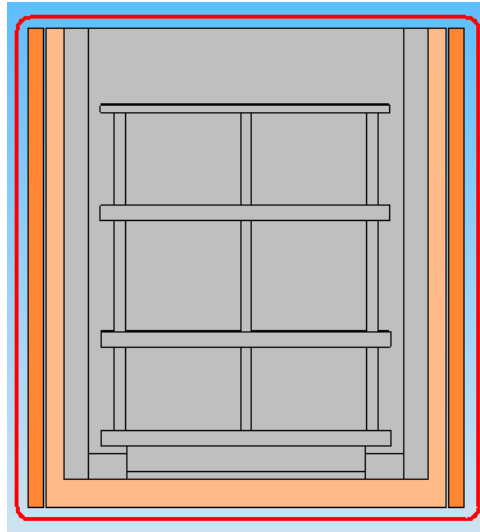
43: Detalle de la colocación de las caras laterales externas de la parte móvil en el cubo
